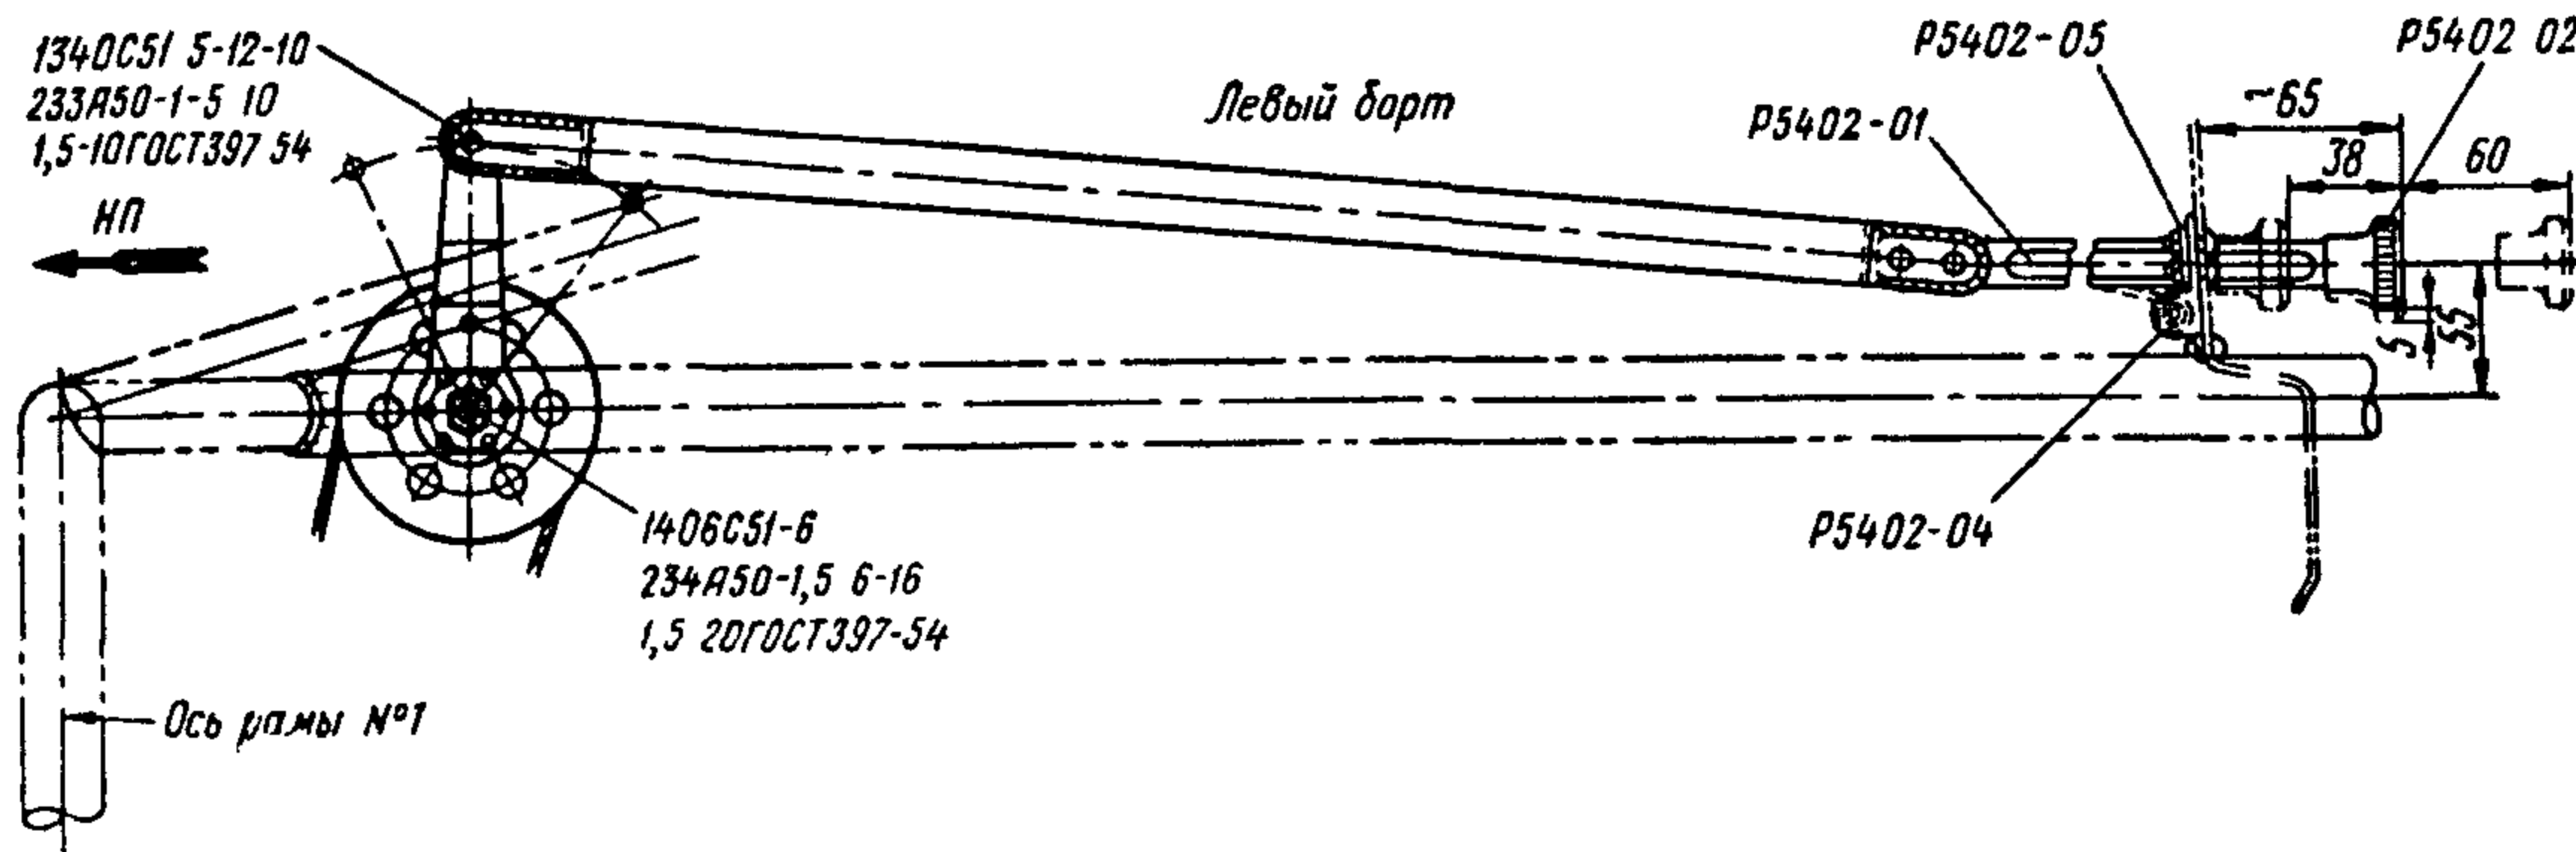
Цилиндр управления закрылками самолета Як-12Р
